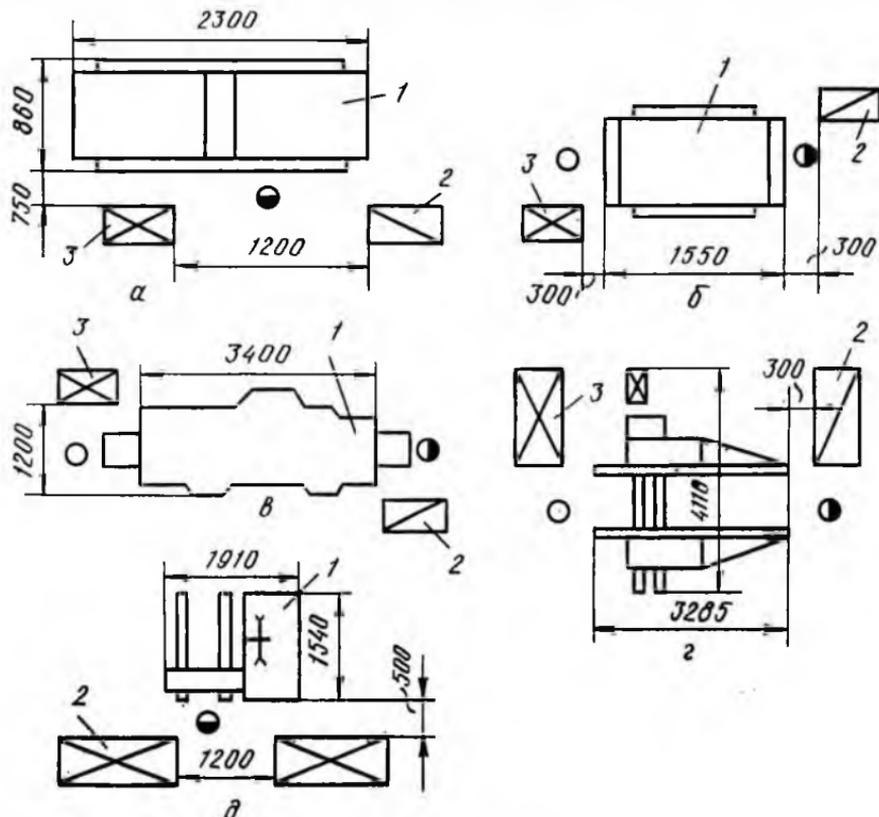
Схема организации рабочих мест станков: а — фуговального; б — рейсмусового; в — четырехстороннего продольно-фрезерного; г — двухпильного торцовочного; д — торцовочного с кареткой; 1 — станок; 2 — контейнер для заготовок; 3 — контейнер для готовых деталей
